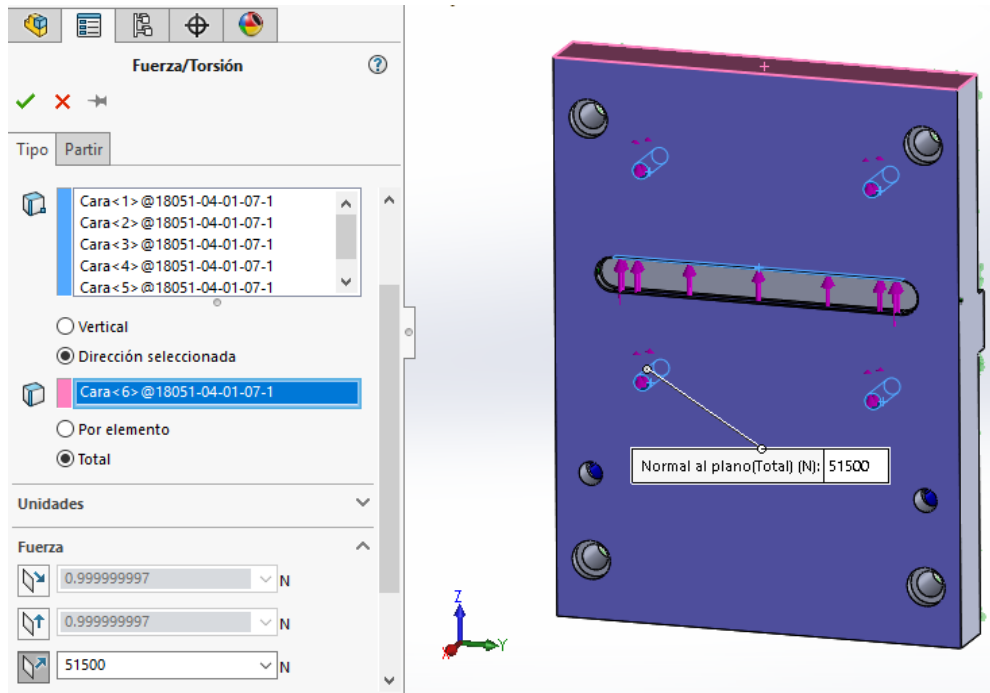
Definición de la Fuerza de inserción a aplicar
